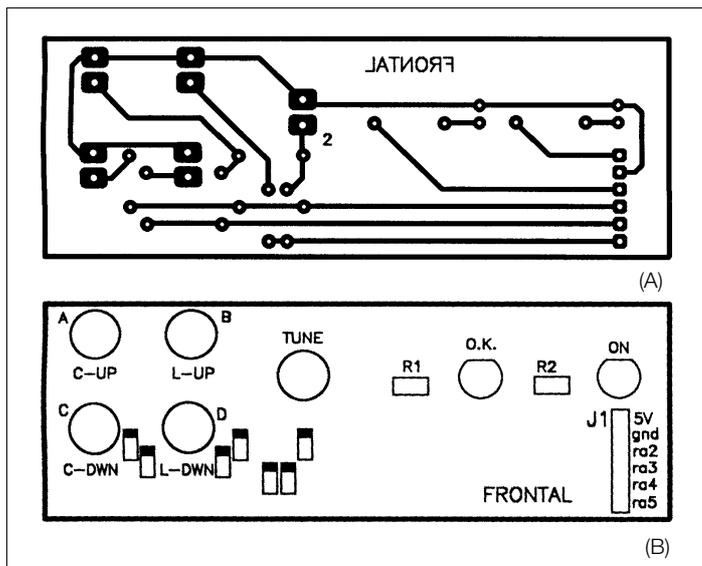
Plantilla de la placa para el panel frontal (A) y disposición de componentes (B).
